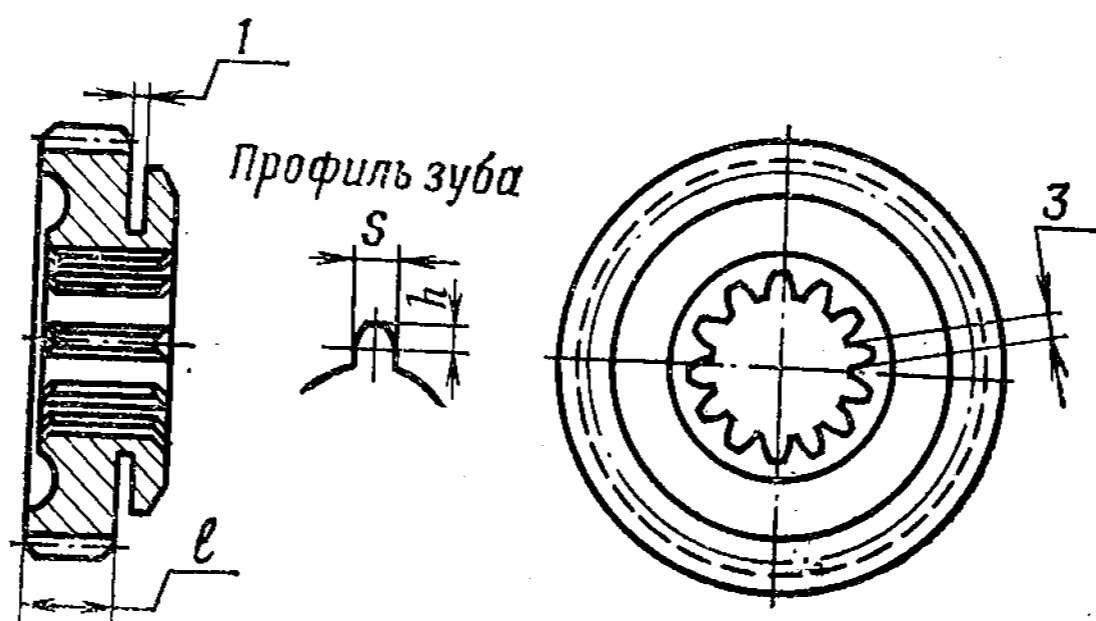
Скользящая шестерня первой передачи и передачи заднего хода
